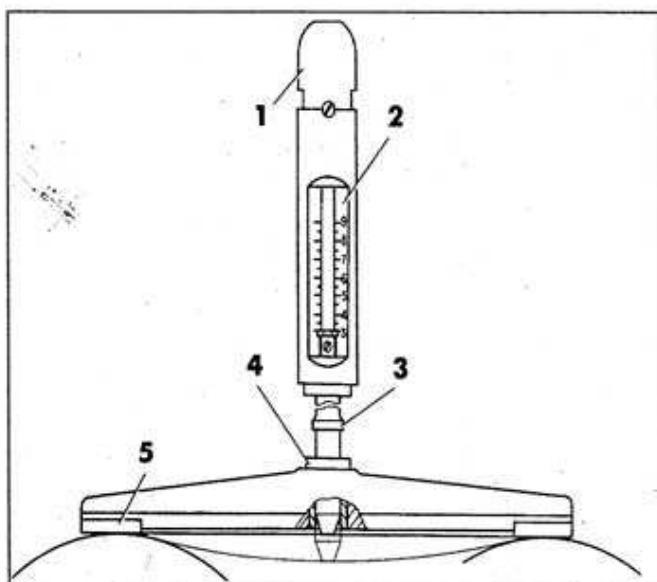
Динамометр 7870-8679 для проверки натяжения ремней привода вентилятора, водяного насоса и генератора:
